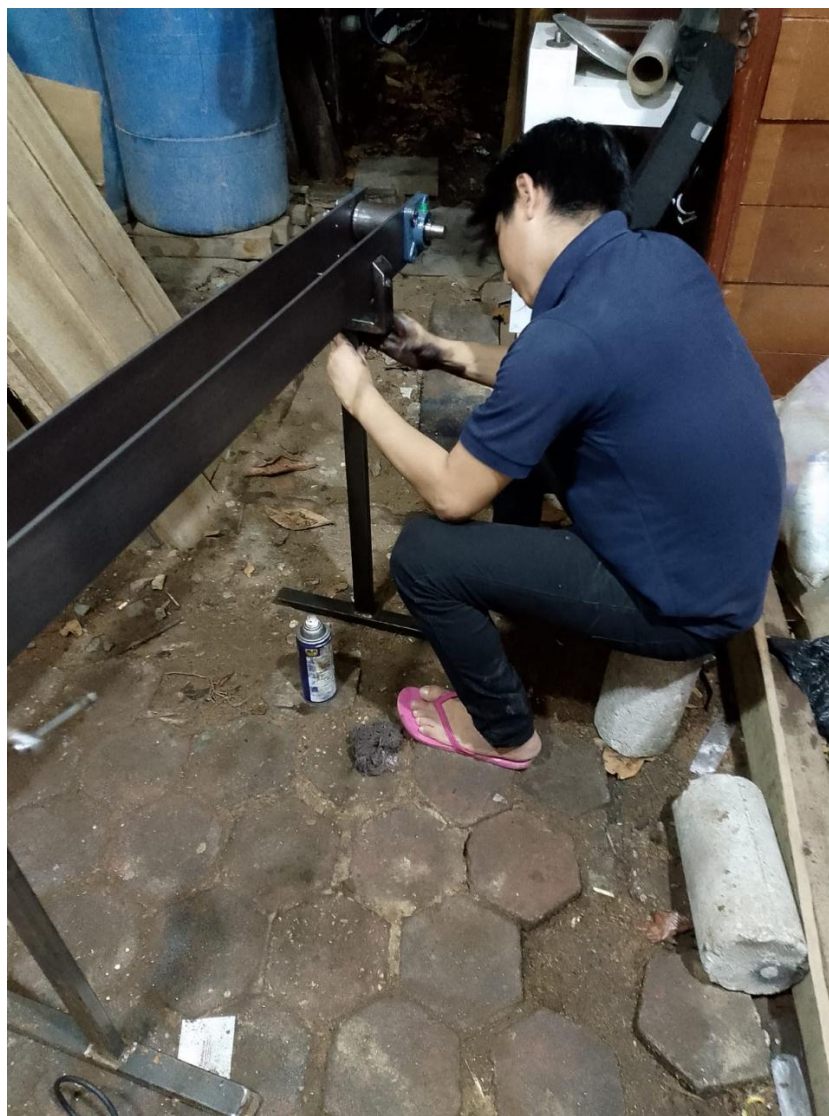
Lijado de estructura. Fuente: Elaborado por autores.
